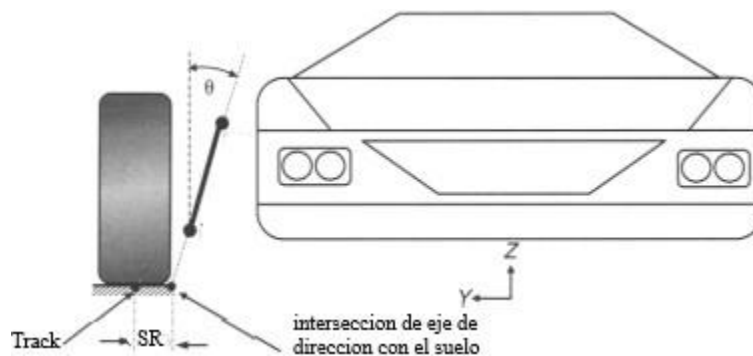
Ángulo de Kingpin y scrub radius [12].
